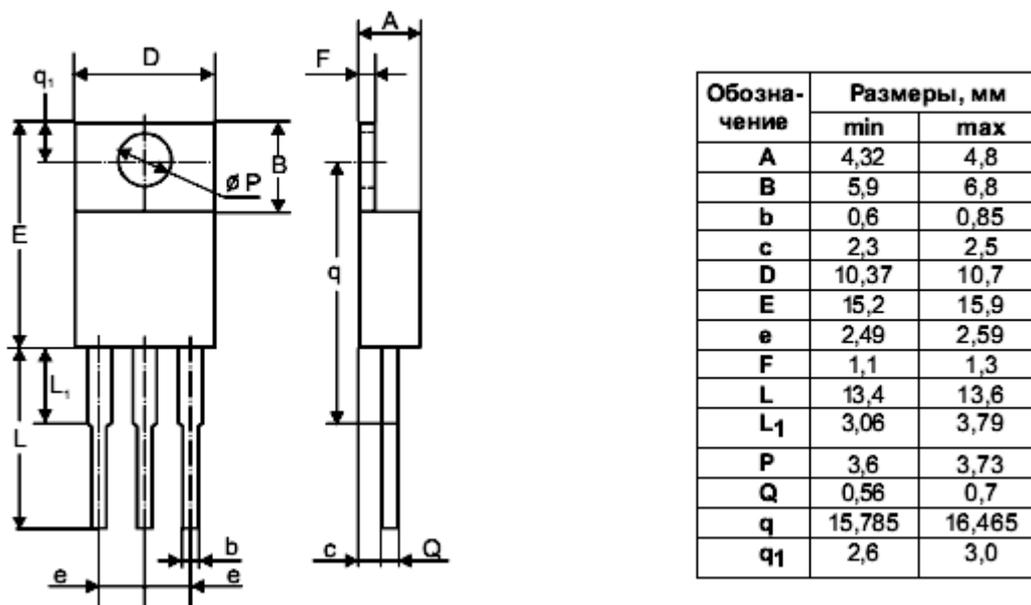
Габаритные размеры корпуса КТ-28-2
